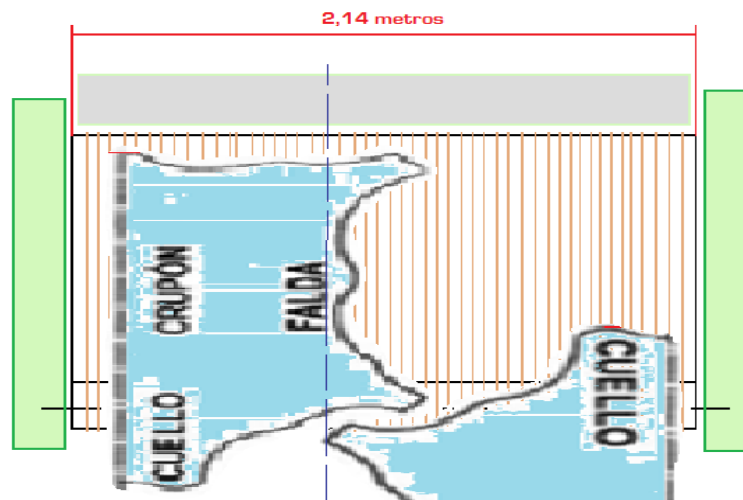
(a). Dimensiones de la Máquina Pigmentadora.
